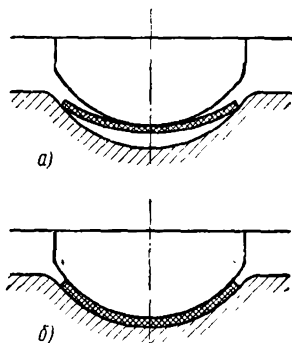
Схема гибки дугообразного элемента: а — промежуточный момент; б — конечный момент
